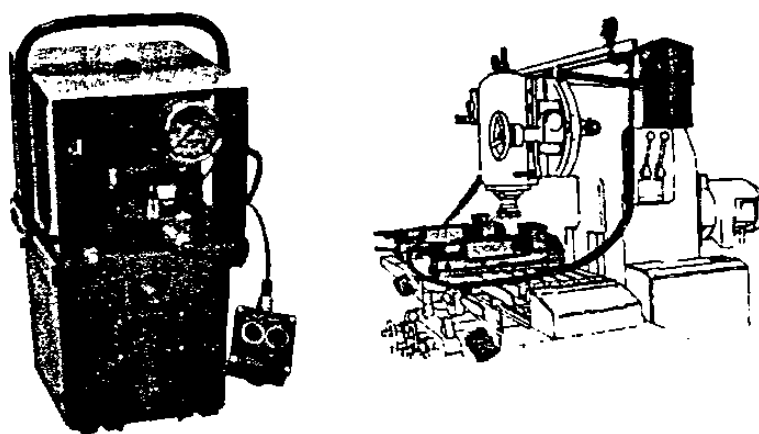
Las unidades eléctricas de poder son una fuente completa de poder hidráulico que incluye una bomba, un dispositivo, válvula e indicador. Estos llegan a ser un accesorio estándar sobre muchas herramientas de máquinas.
